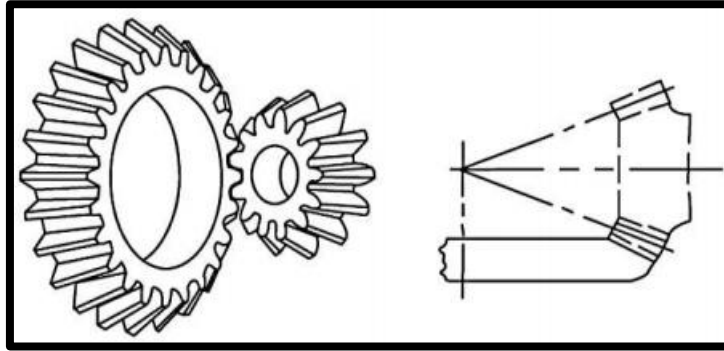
Ejemplo de dos engranajes cónicos de dientes rectos. Fuente: Robert L. Mott[23].
